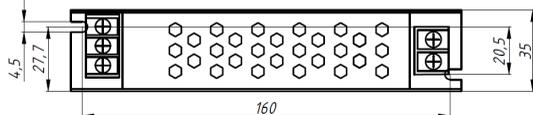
Габаритные размеры блока питания Geniled GL-12V60WM20 Slim.
